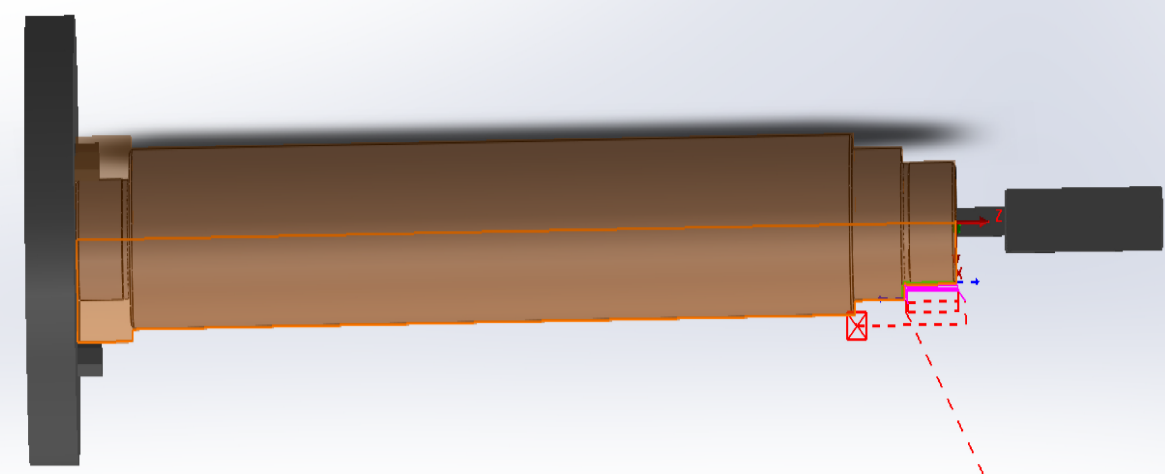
Чорнова та чистова обробка поверхні $\varnothing 35k6$
